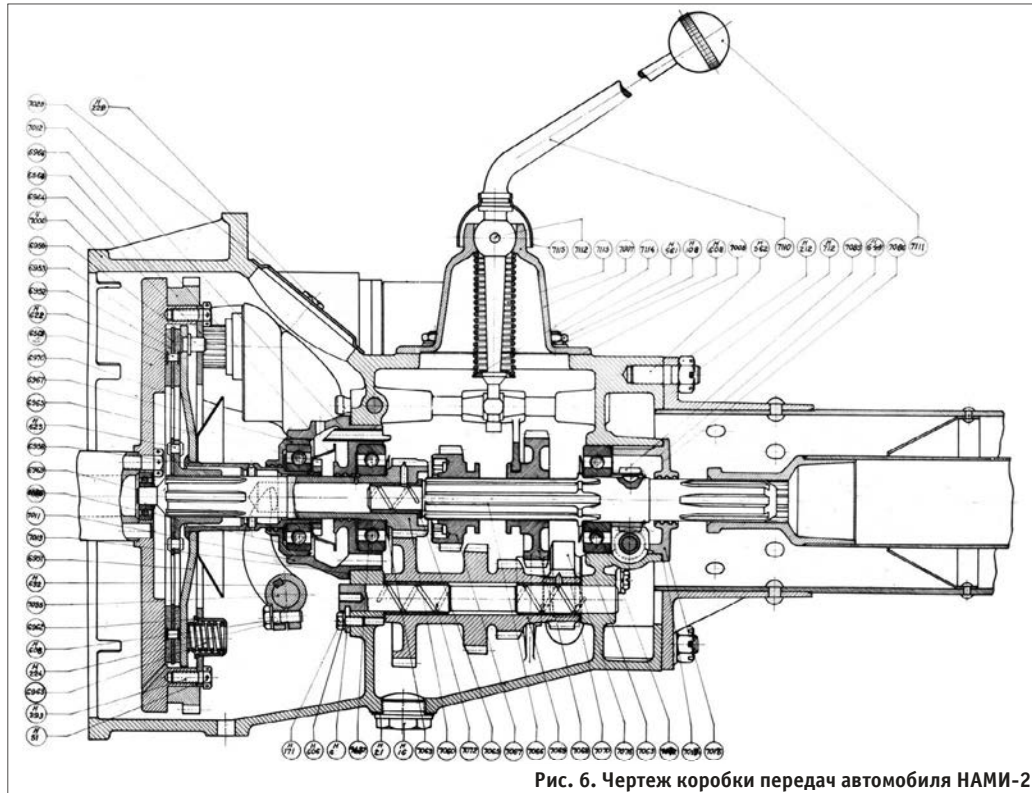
Чертеж коробки передач автомобиля НАМИ-2
